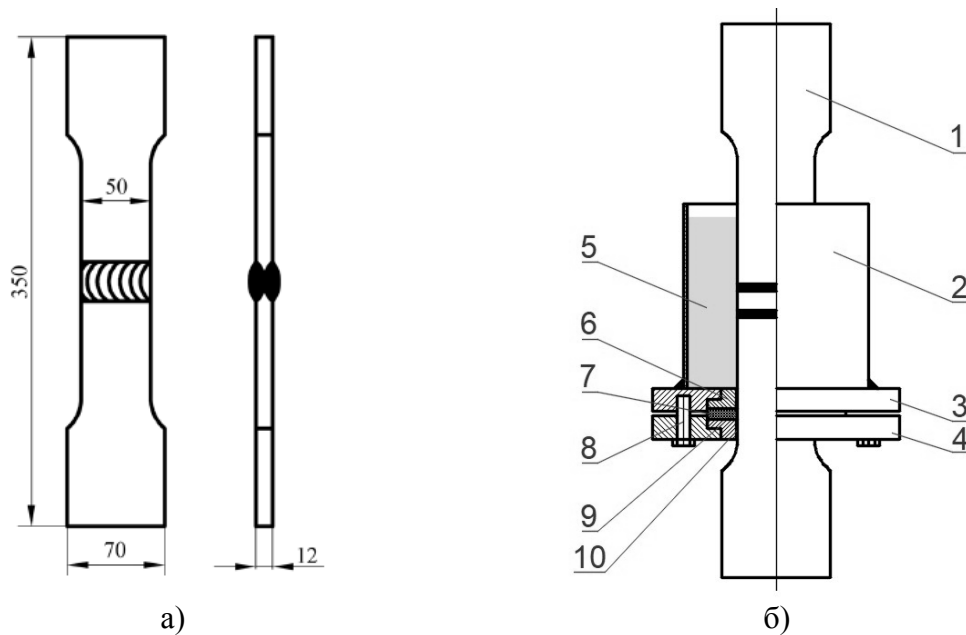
Форма і геометричні розміри зразків (а) та схематичне зображення оснащення для випробувань зварних з'єднань на корозійну втому при одновісному розтягу (б): 1 – зразок; 2 – камера; 3 – основа корпусу камери; 4 – плита; 5 - робочий розчин; 6- вставка (сухарик) в корпус камери; 7 – гумова прокладка; 8 – болт; 9 - вставка (сухарик) в плиту; 10 – силікон.
